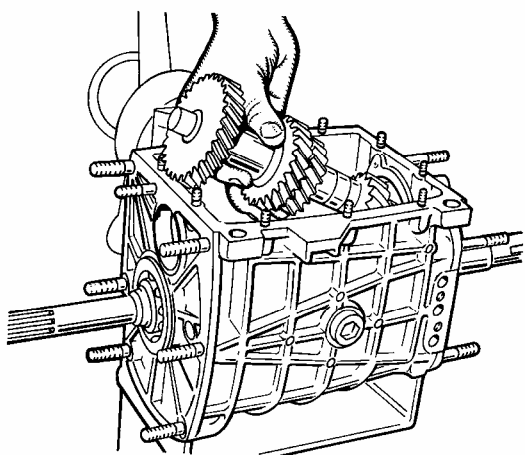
Извлечение промежуточного вала из картера коробки передач
